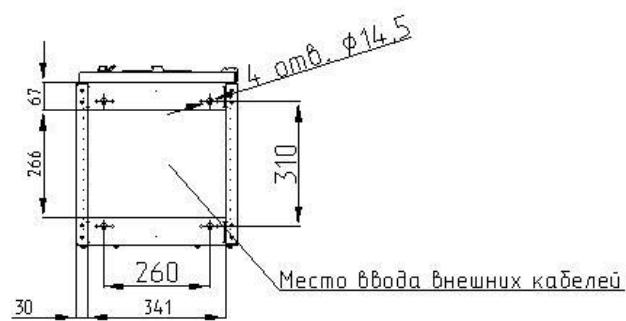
Габаритный чертеж шкафа управления и защит
